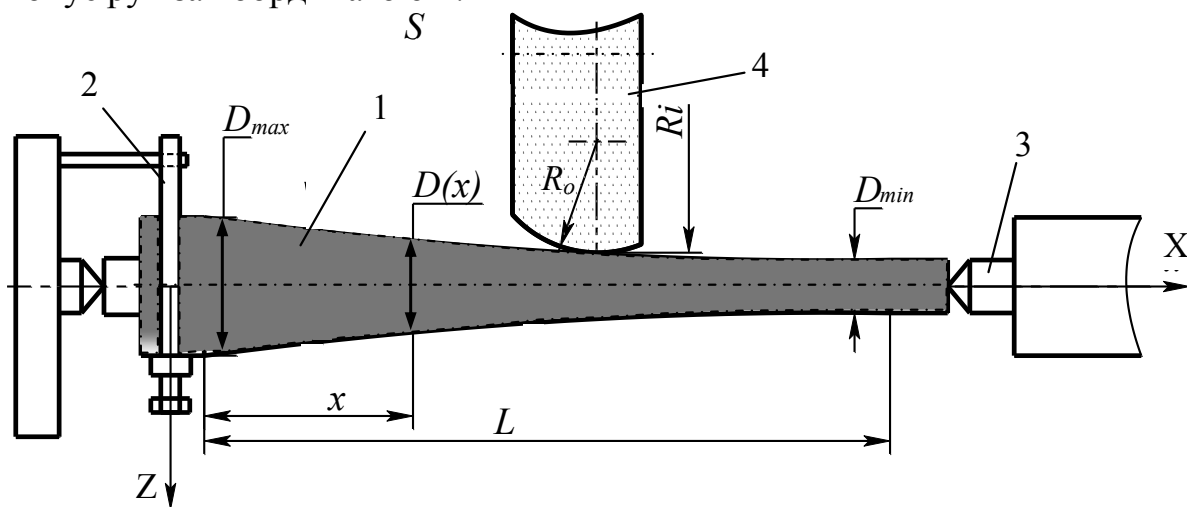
Схема шліфування поверхні оправки на верстаті з ЧПК
